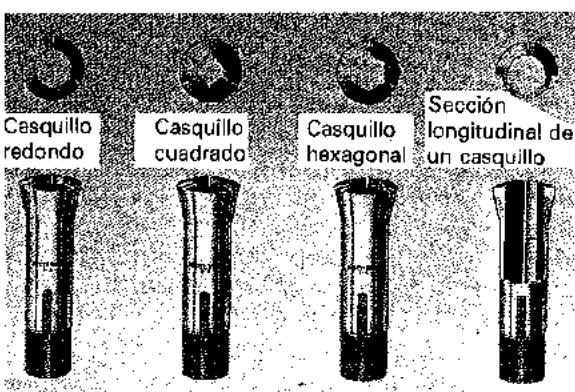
Casquillos elásticos para diferentes perfiles de barra (South Bend Lathe Works).
